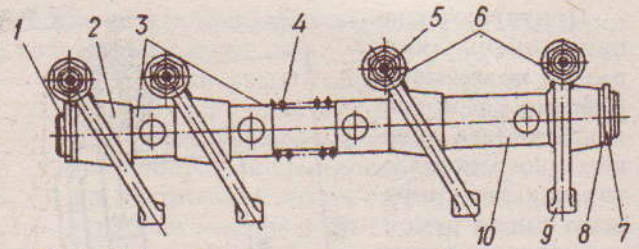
Валик коромысел клапанов в сборе: 1 - валик коромысел; 2 - коромысло левое; 3 - втулка; 4 - пружина распорная; 5 - винт регулировочный; 6 - гайка; 7 - шплинт; 8 - шайба; 9 - коромысло правое; 10 - втулка распорная
